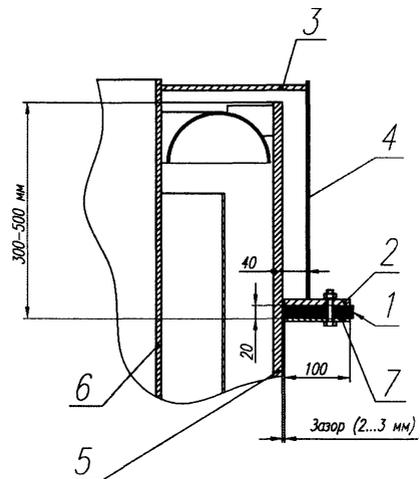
Схема компенсатора: 1 – жаростойкая ткань; 2 – фланец; 3 – кольцо; 4 – обечайка; 5 – корпус вагранки; 6 – корпус рекуператора; 7 – прижимной фланец
